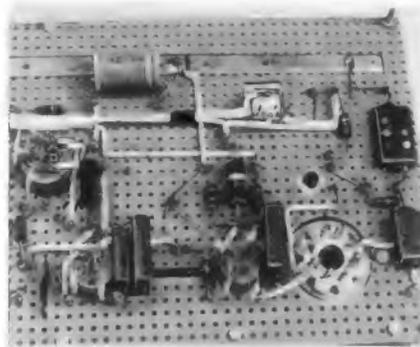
Ausschnitt aus einer mit Picofix aufgebauten Schaltung
